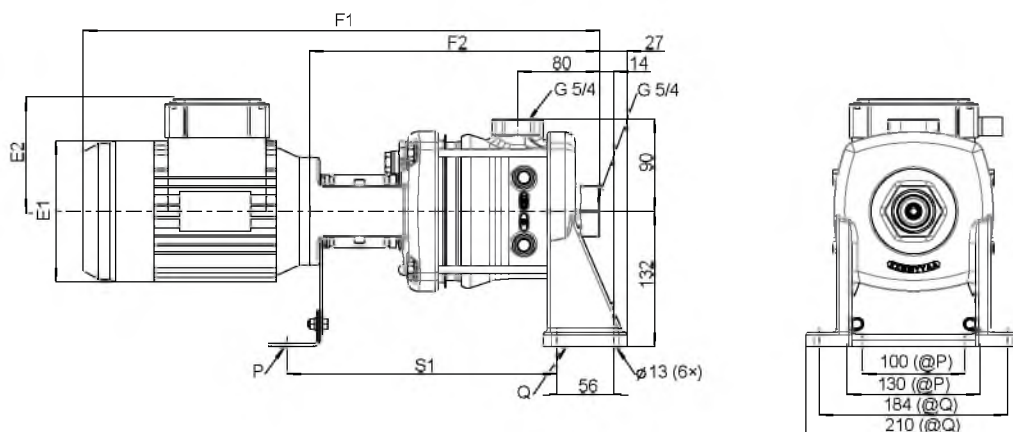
Размеры и подсоединения Movitec H(S)I 2 с двигателем V18²⁴⁸⁾
